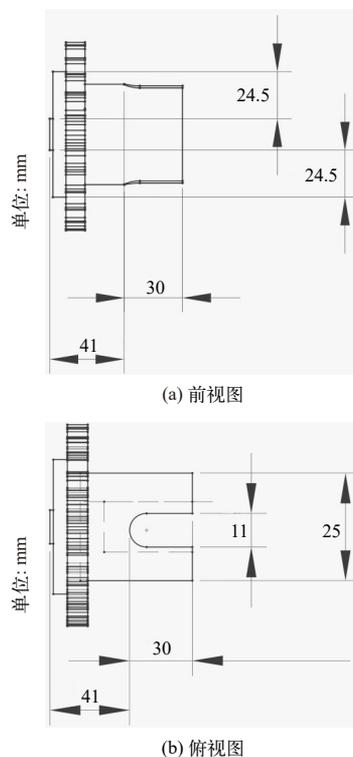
基于 Shapr3D 实现的液压弹簧断路器齿轮连接固定装置投影视图
